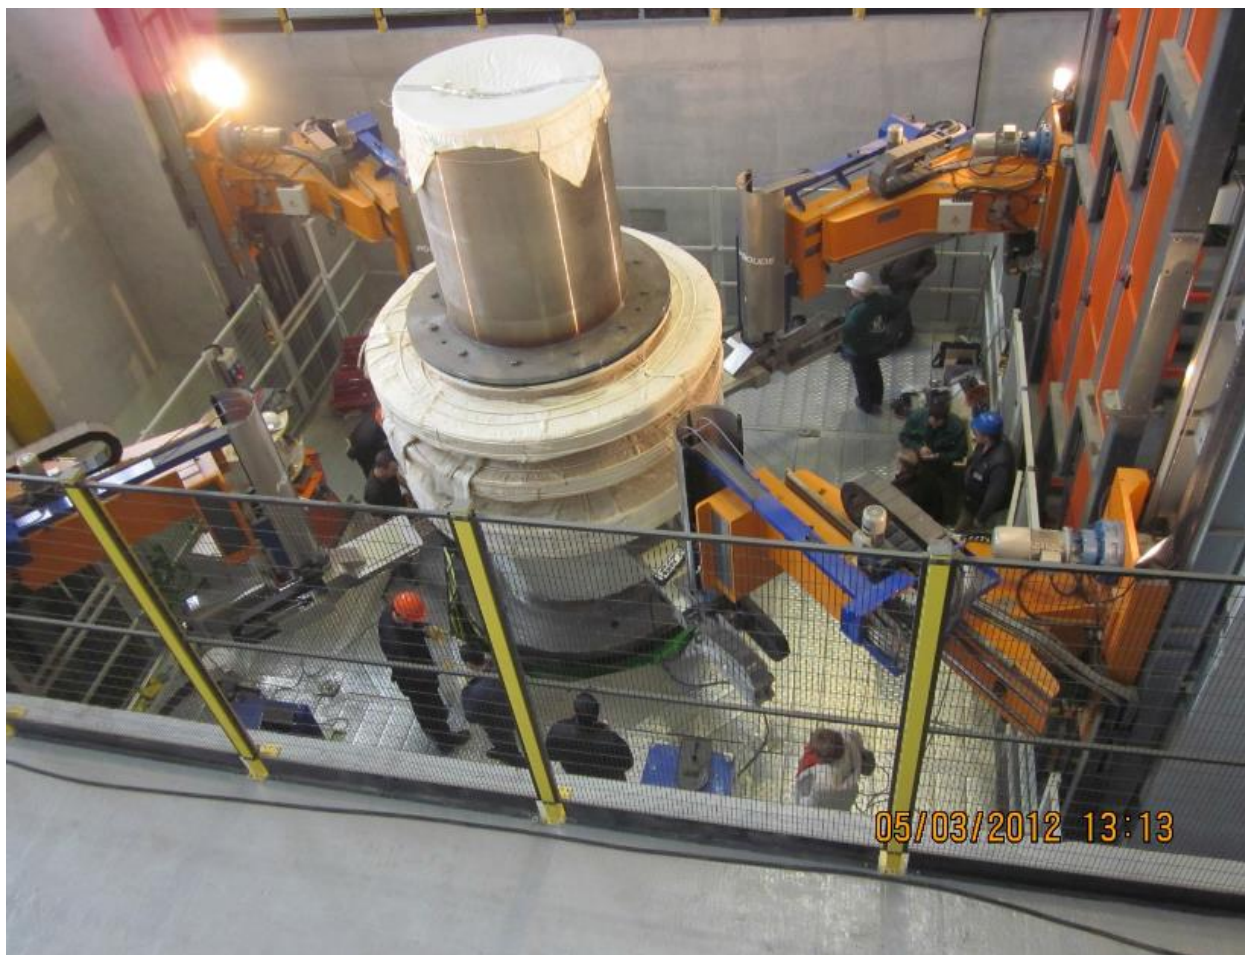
Сварка ротора тихоходной турбины четырьмя сварочными головками в узкую разделку в поворотном положении
